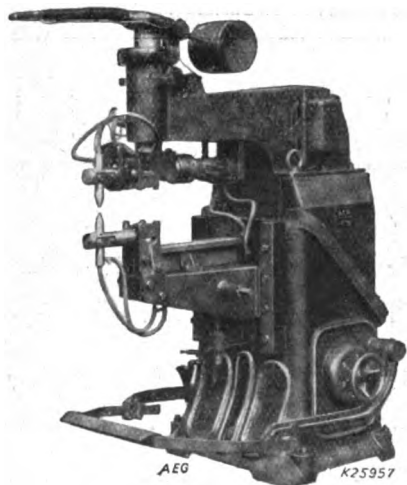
Hochleistungs-Punktschweißmaschine.
